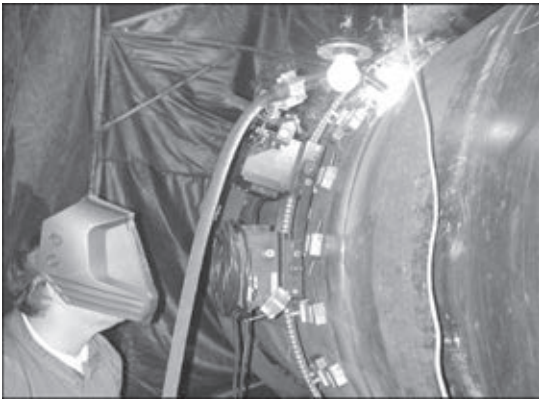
Система сварки неповоротных швов фирмы «CRC Evans» (США)
